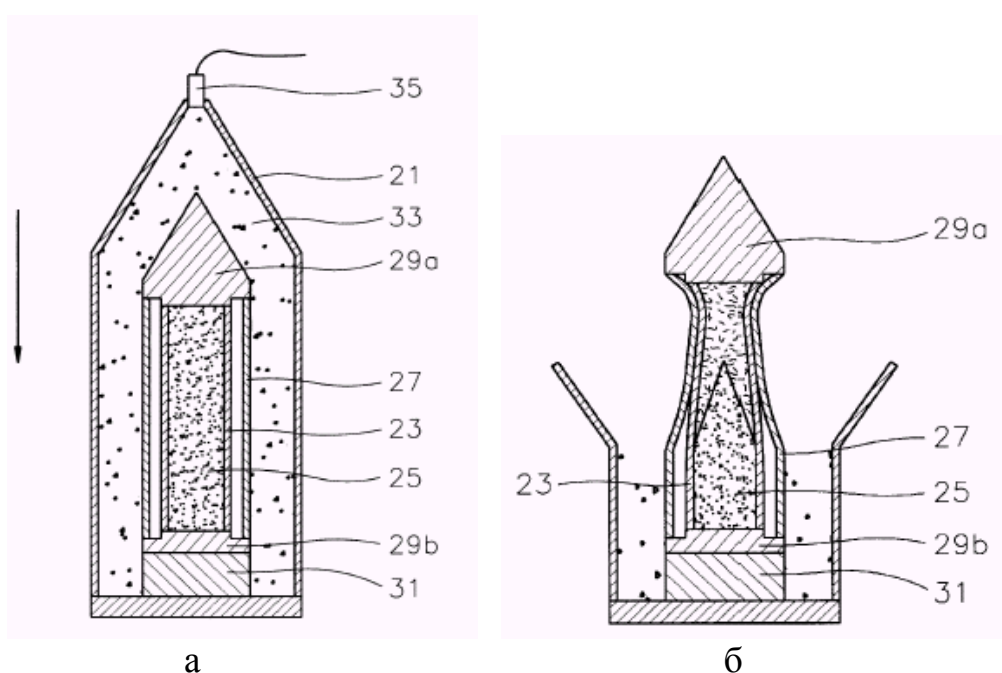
Схема получения заготовки из бериллиевой бронзы по патенту № KR100292119B Южнокорейского института машиностроения и металлургии KOREA MACHINERY & METAL INST: а – сборка до взрыва; б – остатки сборки после взрыва
